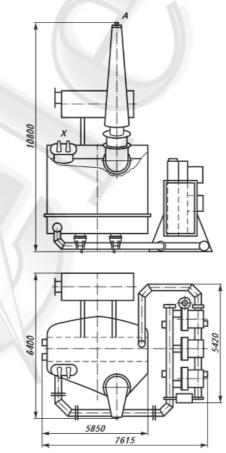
Общий вид и габаритные размеры реактора типа РОДЦ-110 000/750-У1
